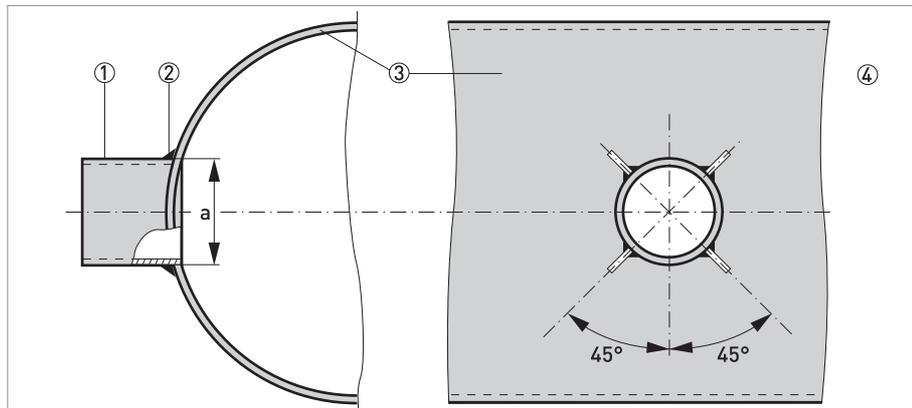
Montaje del extremo de soldadura con tiras de hierro
